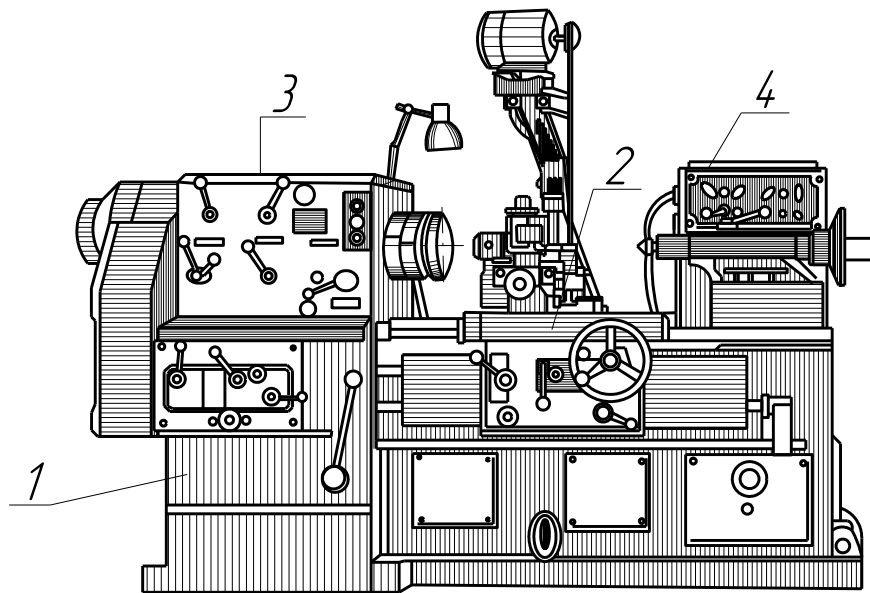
Універсальний токарно-затилувальний верстат 1E811
